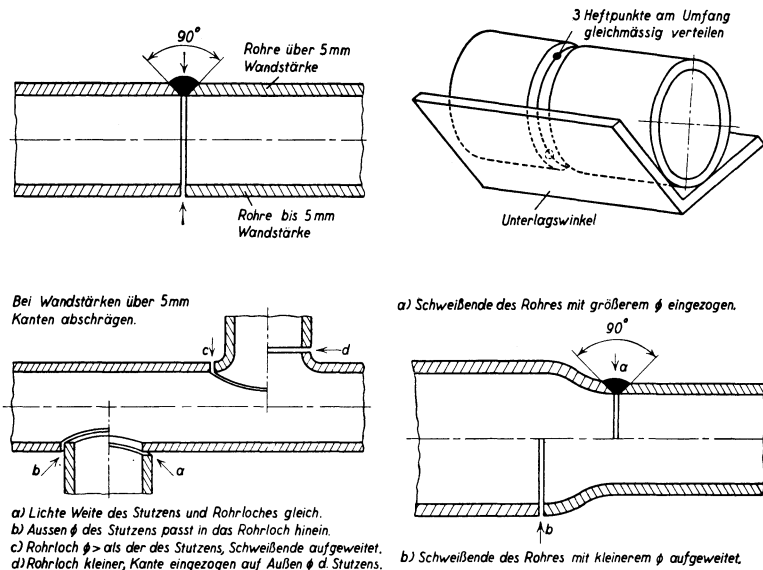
Rohrverbindungen durch Schweißen.
